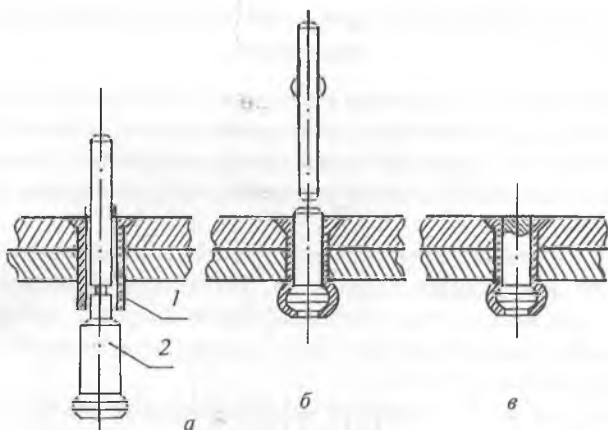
Заклепка с сердечником: *а* — вид заклепки до клепки; *б* — расклепанная заклепка; *в* — заклепка со срезанной выступающей частью стержня; 1 — пистон заклепки; 2 — стержень заклепки
